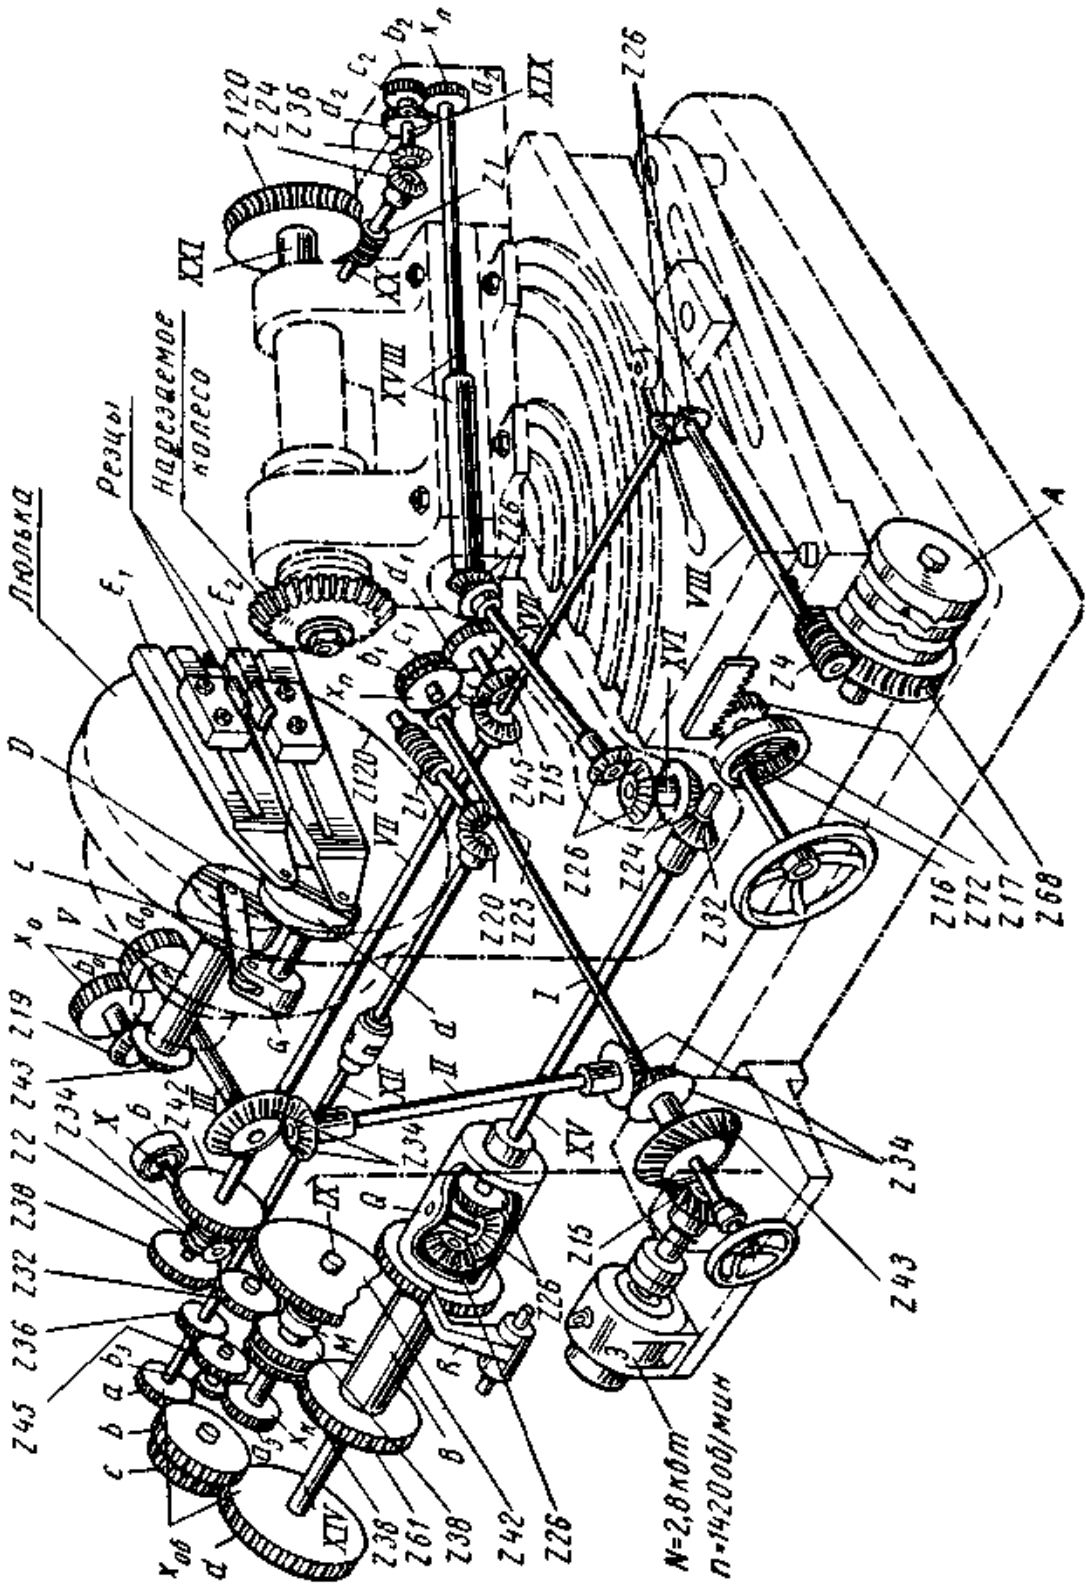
Кинематическая схема зубострогального станка мод. 526
